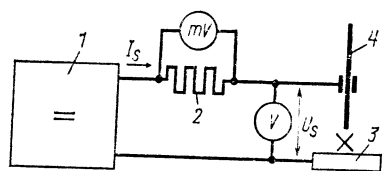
Измерение сварочного тока  $I_s$  и напряжения  $U_s$  при сварке на постоянном токе:
